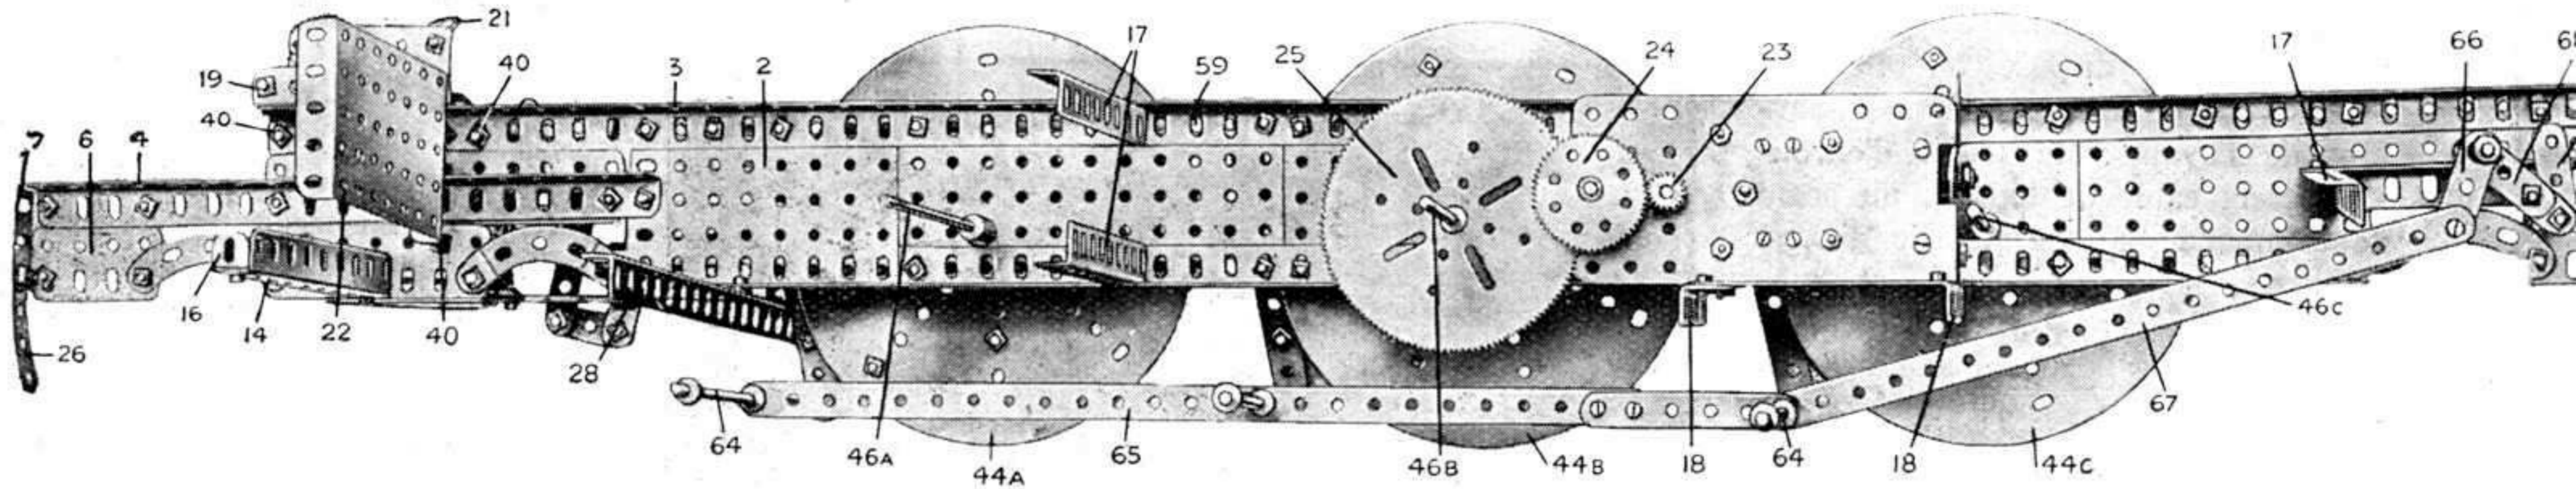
Vue intérieure du côté droit du châssis montrant la position du Moteur et des Engrenages démultiplicateurs.
